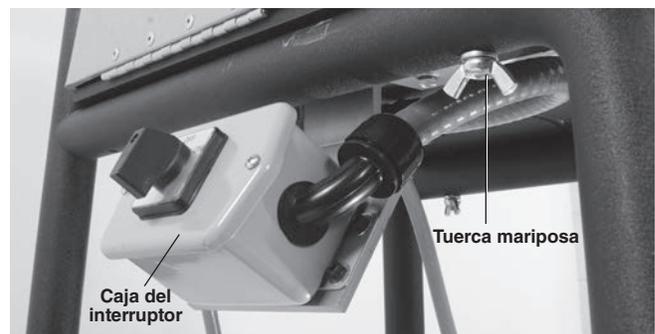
Montaje de la ranuradora a rodillos sobre el soporte
